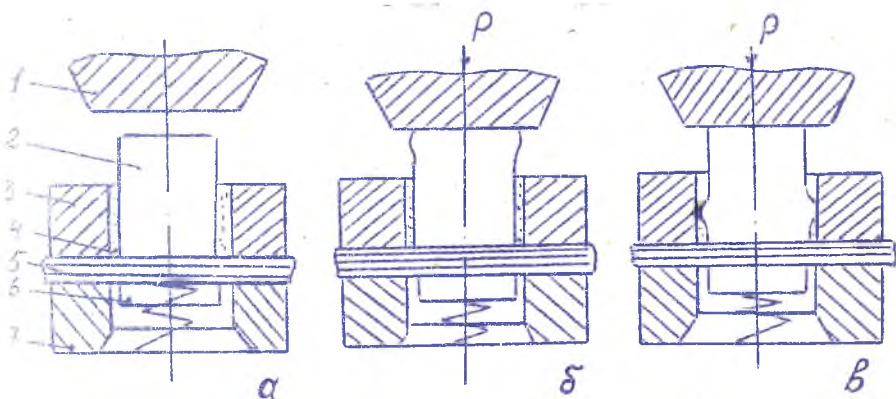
Схема гидродинамической пробивки отверстия: 1 – ударник; 2 – пуансон; 3 – направляющая плита; 4 – вязкая среда; 5 – заготовка из ПКМ; 6 – упругий элемент; 7 – матрица
